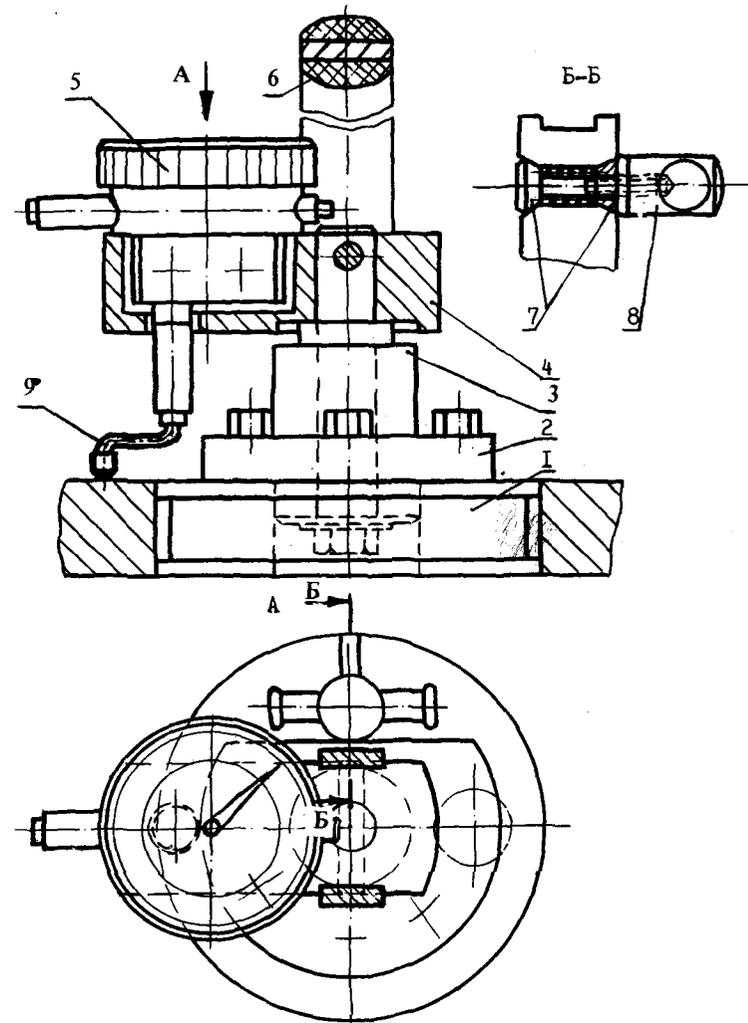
Контрольное приспособление для проверки торцового биения:
